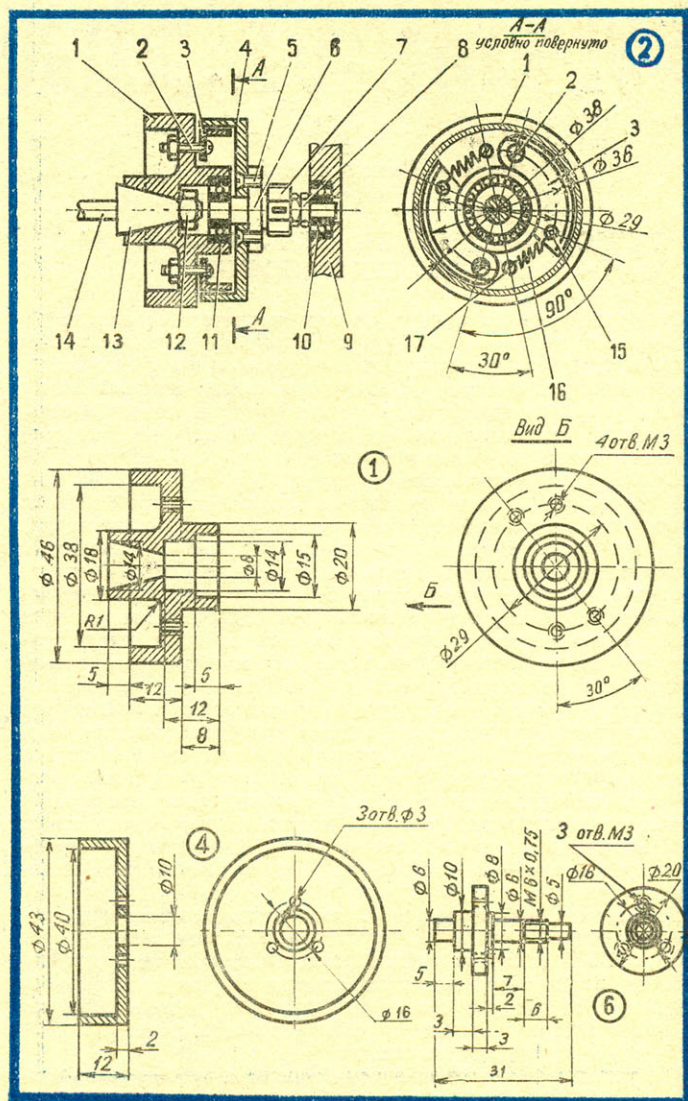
Устройство автоматического сцепления традиционного типа (на двигателях 2,5–3,5 см³): 1 — маховик, 2 — винты крепления колодок, 3 — колодка сцепления, 4 — ведомый барабан сцепления, 5 — винт, 6 — ведомая ось, 7 — шестерня, 8 — гайки, 9 — стойка (крепится отдельно к кузову), 10 — подшипник 5×13, 11 — подшипник 6×16, 12 — гайка крепления маховика, 13 — конусная шайба, 14 — ось мотора, 15, 17 — винты М3, 16 — стяжная пружина.
